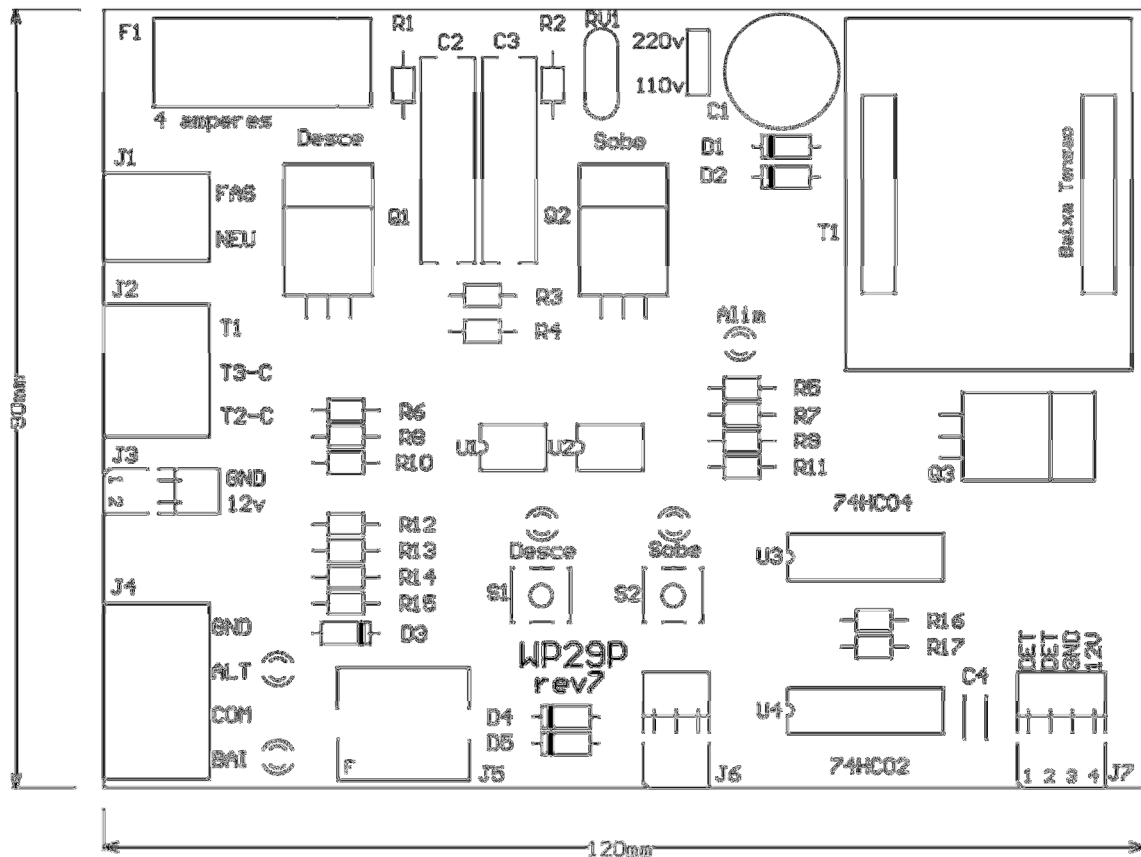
Esquema de Montagem de Componentes da Placa WP29
